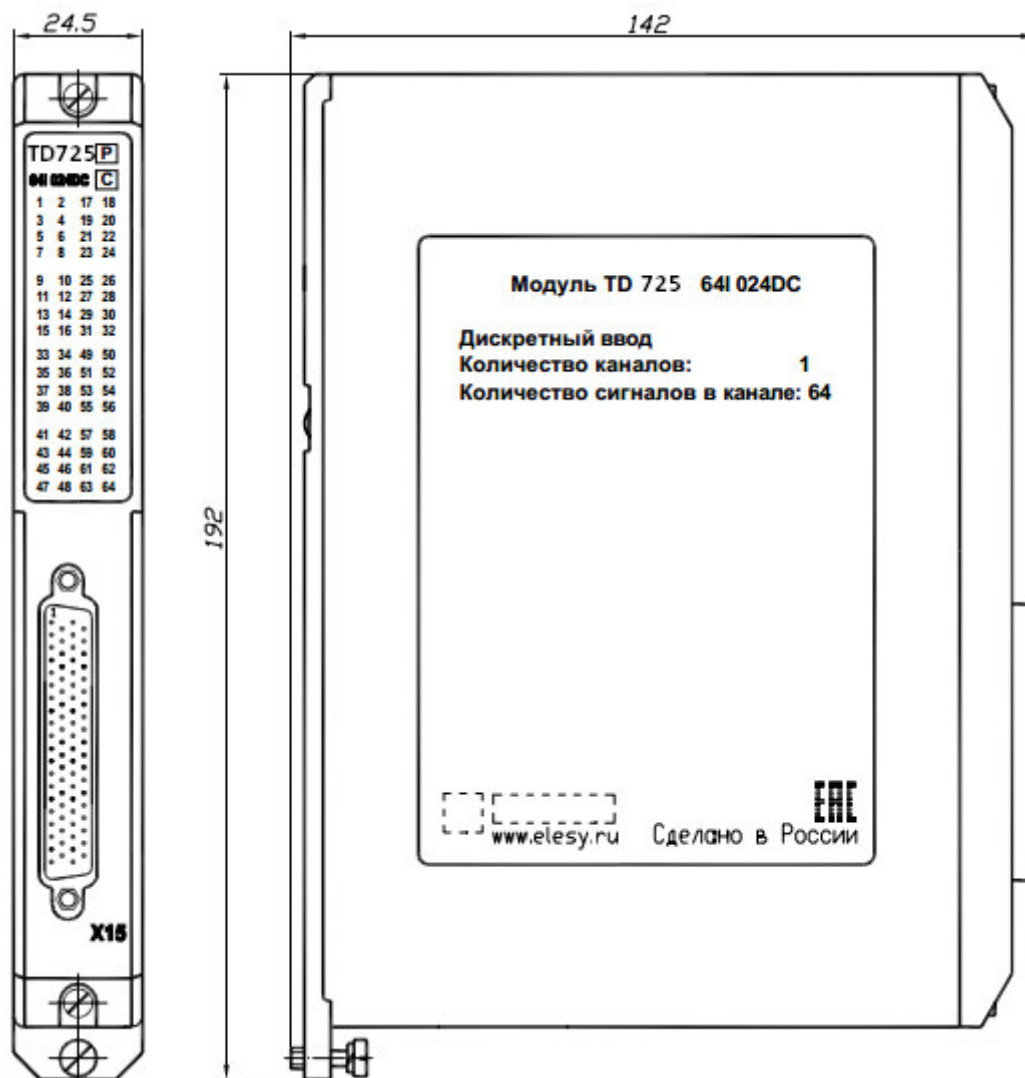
Внешний вид и габаритные размеры модуля
